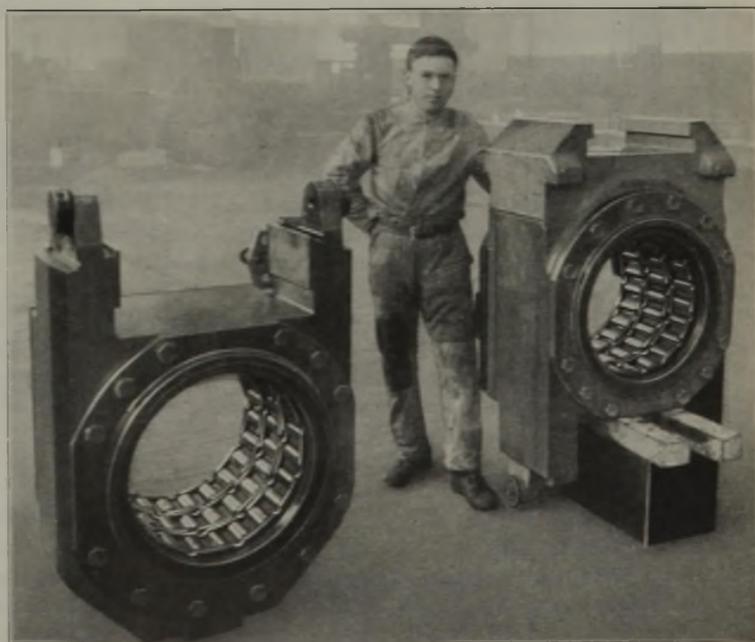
Stützwalzenlagerung eines Vierwalzen-Kaltwalzgerüsts. Walzdruck 420 t.
